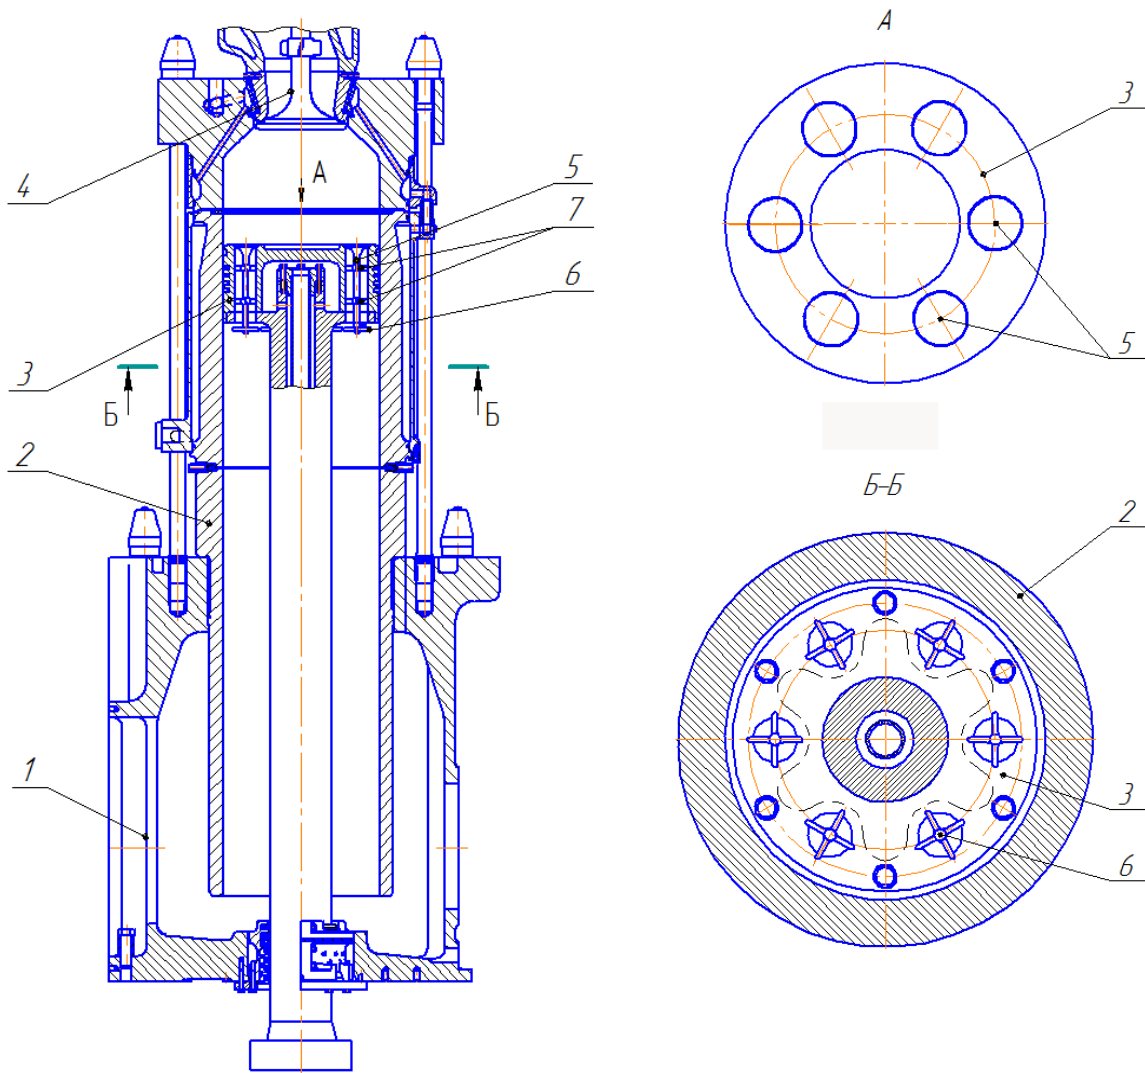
Загальний вигляд прямоточно-клапанної системи газообміну двотактного дизеля: 1 – ресивер продувного повітря; 2 – циліндрова втулка; 3 – поршень; 4 – випускний клапан; 5 – продувні клапани; 6 – стопор; 7 – крилатки
